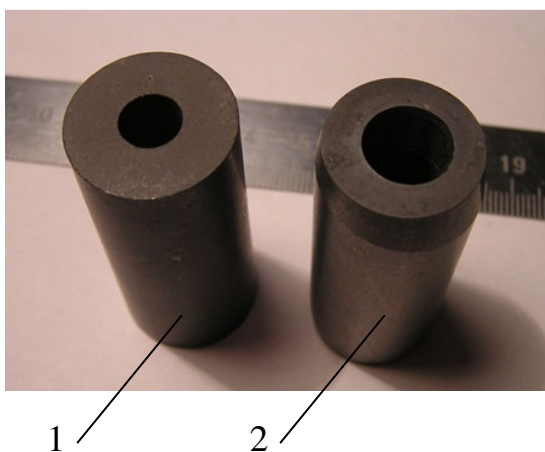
Обработанная деталь-«матрица»: 1 – до обработки; 2 – после обработки
